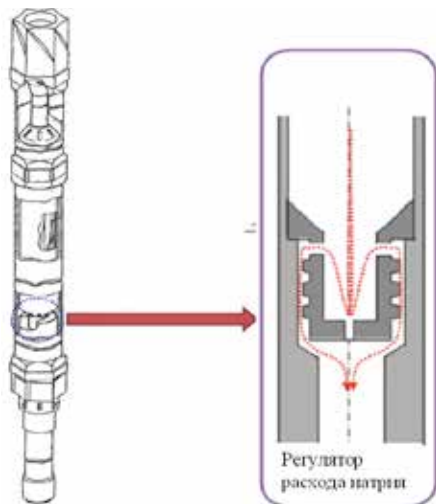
Общий вид конструкции регулирующей сборки реактора и регулятора расхода натрия
